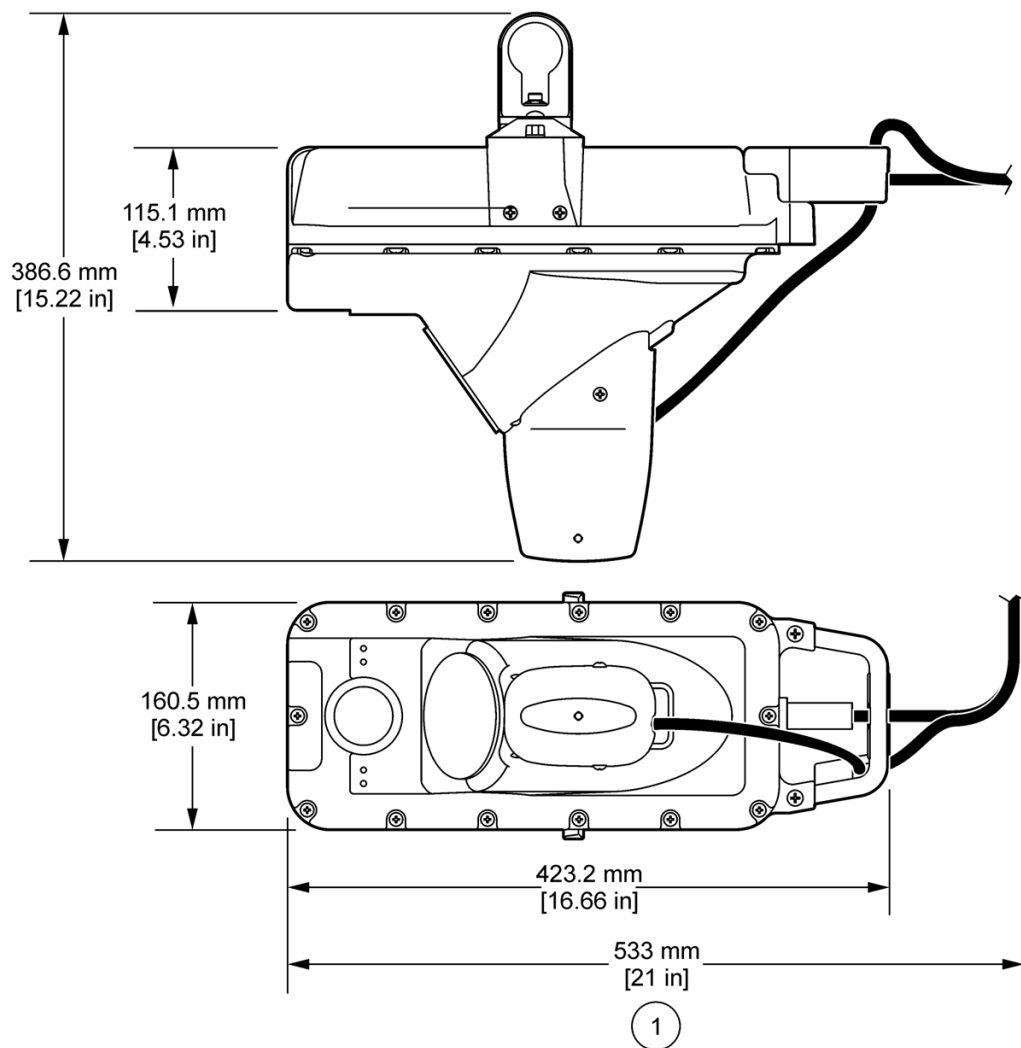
Dimensiones del sensor Flo-Dar con el SVS
